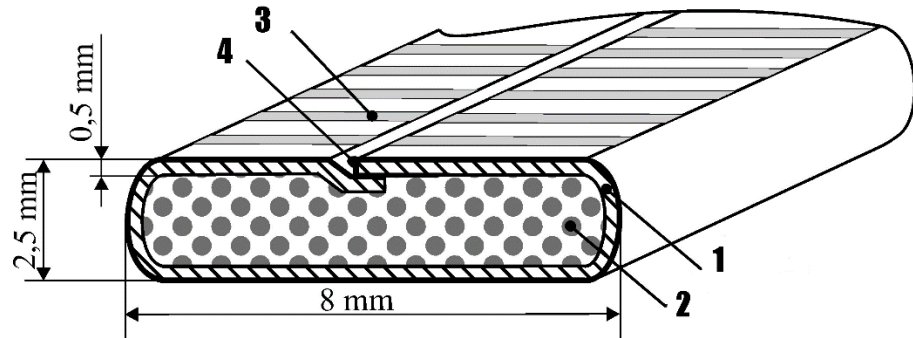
Конструкція порошкової стрічки: 1 – металева оболонка; 2 – порошкова суміш (шихта); 3 – рифлення електрода; 4 – напустковий замок
